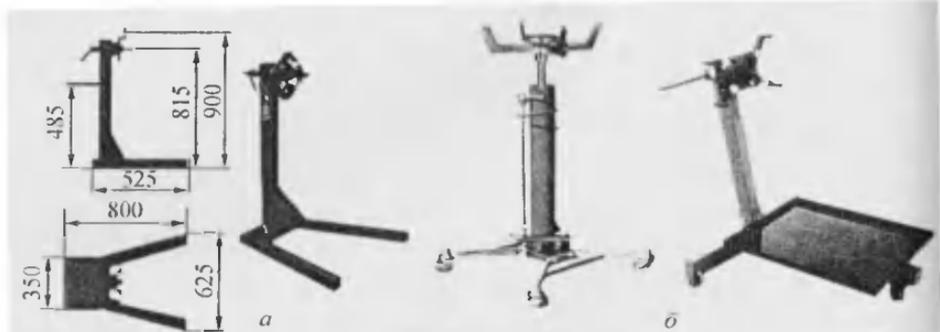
Стенды для снятия и установки коробок передач (а), разборки и сборки редукторов ведущих мостов (б)
